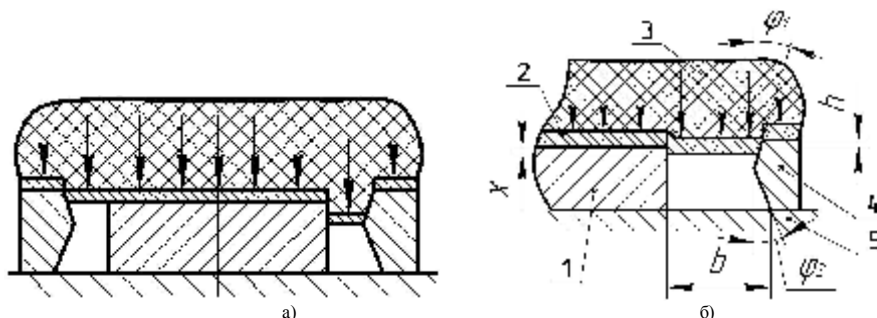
Конструктивно-технологическая схема основных этапов вырубki деталей с боковым обжатием заготовки:
